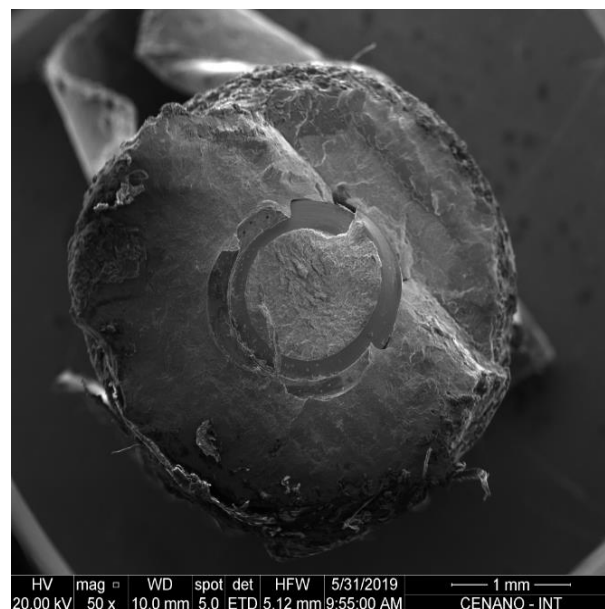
Vista superior do implante fabricado por manufatura aditiva (SLM), após fratura (MEV).
